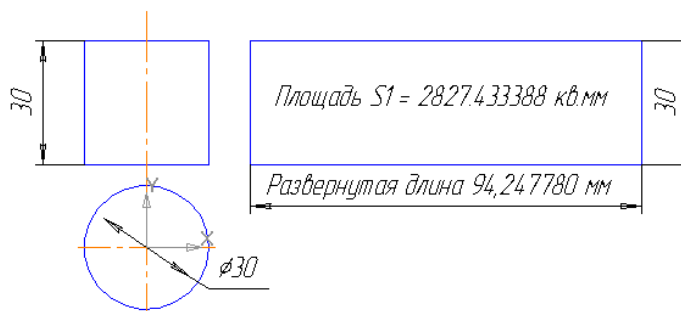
Проекция цилиндра и развертка его боковой поверхности
